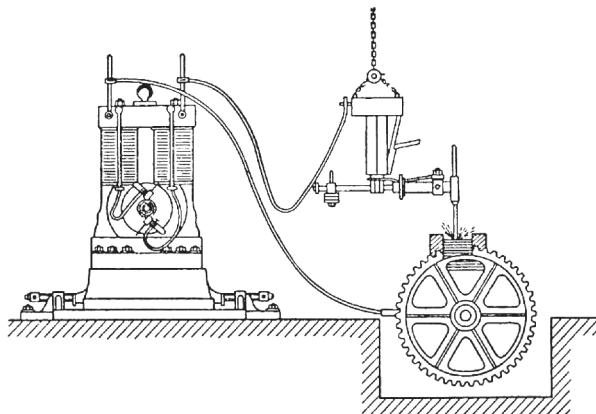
Схема дуговой электросварки по способу Н.Г. Славянова.
